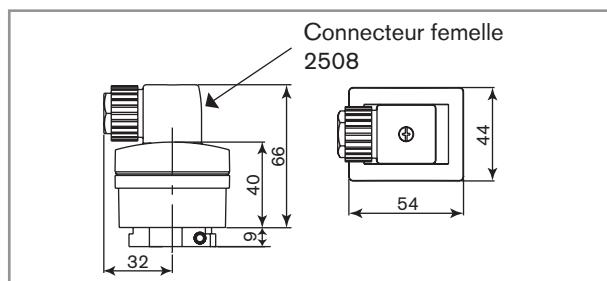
Dimensions [mm] du module électronique SE30 Ex
